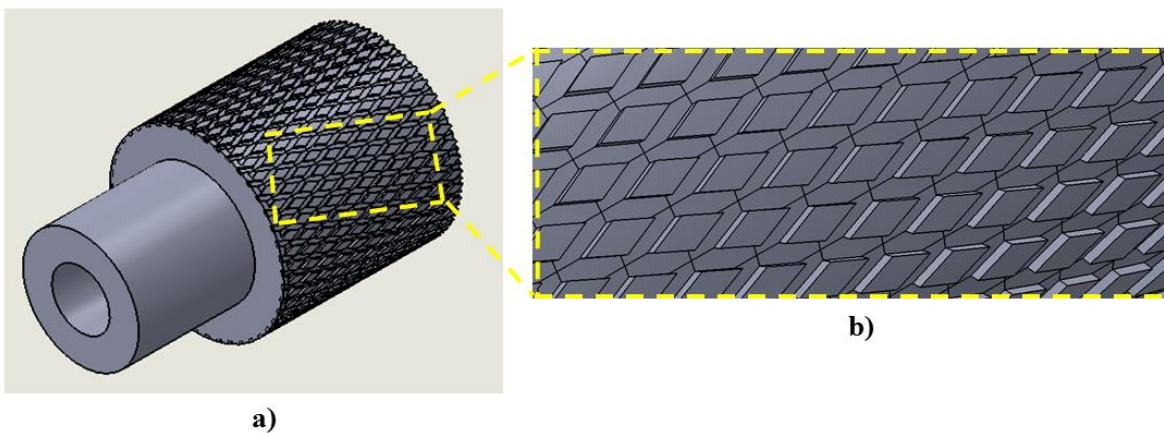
a) Vista isométrica de la cabeza del tornillo, b) Operación del moleteado realizada en la cabeza de los tornillos para poder tener un mejor agarre.
